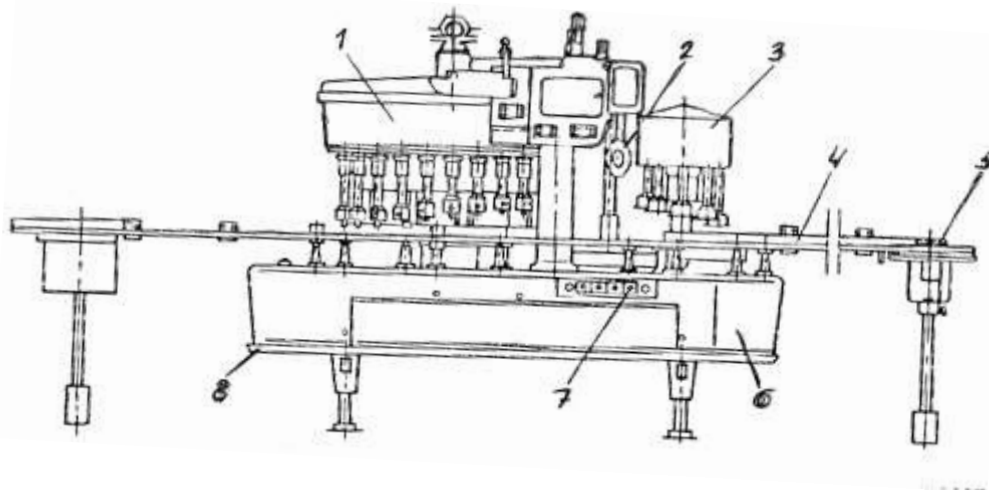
Загальний вигляд фасувально-закупорювального автомата типу И2-ОРК-3: 1- розливальна головка; 2- штамп; 3- закупорювальна головка; 4- напрямні; 5- поворотна головка; 6- обшивка корпусу; 7- кнопки електрообладнання; 8- жолоб для збирання молока.
